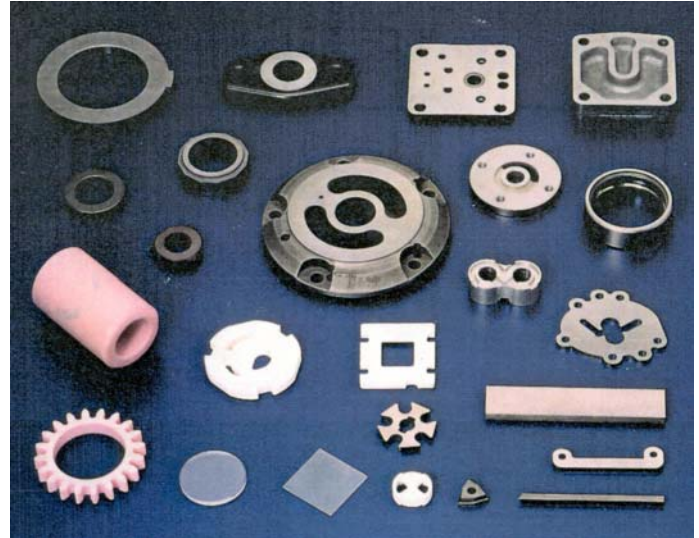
Werkstücke, bearbeitet auf 2-Scheiben Maschinen
